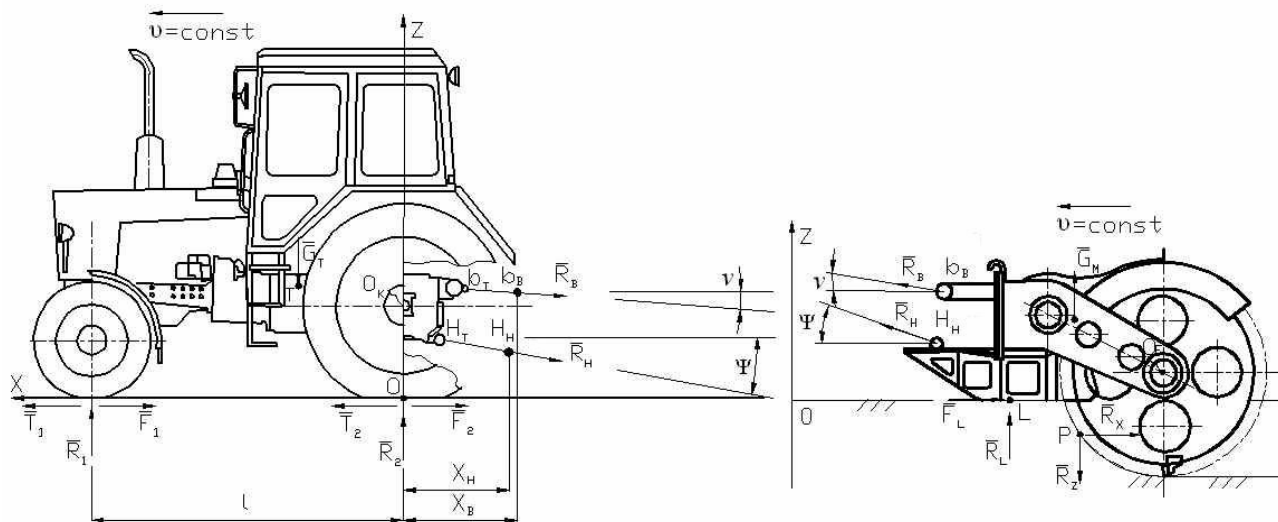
Расчетная схема фрезерующего тракторного агрегата
